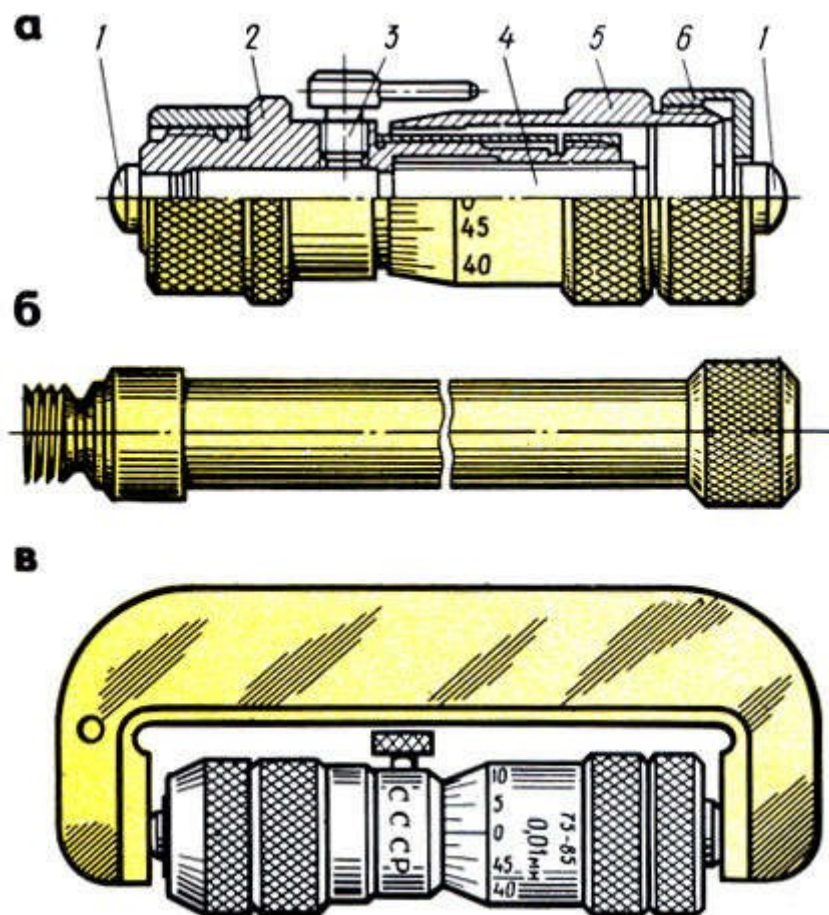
Микрометрический нутромер (штихмасс): а - устройство, б - удлинительный стержень, в - проверка нулевого положения; 1 - измерительные поверхности, 2 - стержень, 3 - стопор, 4 - микрометрический винт, 5 - барабан, 6 - гайка
